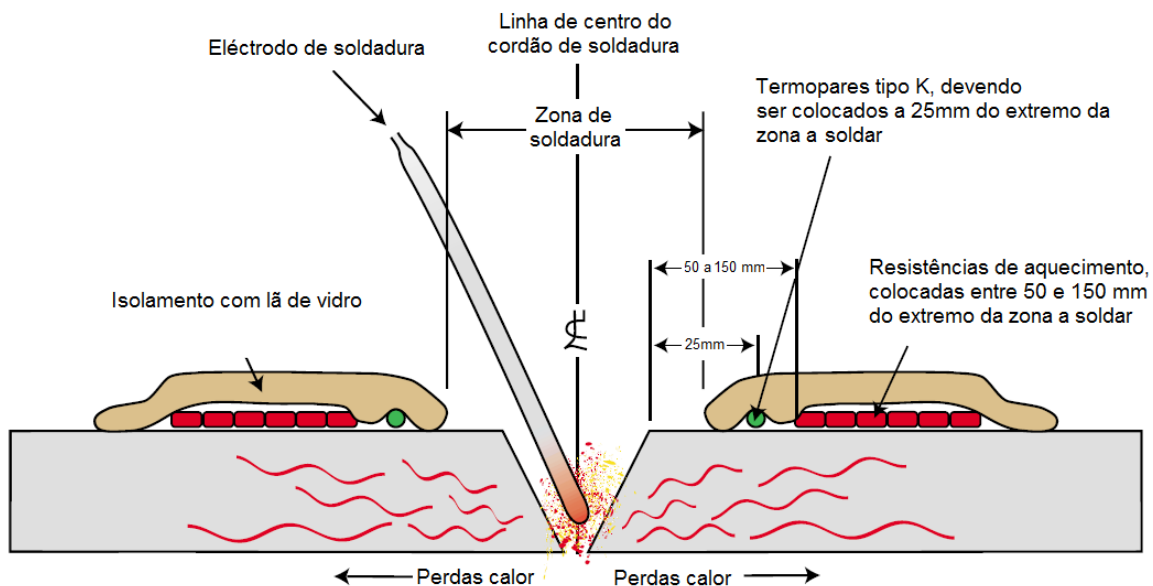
Esquema de montagem de um pré-aquecimento de soldadura.
